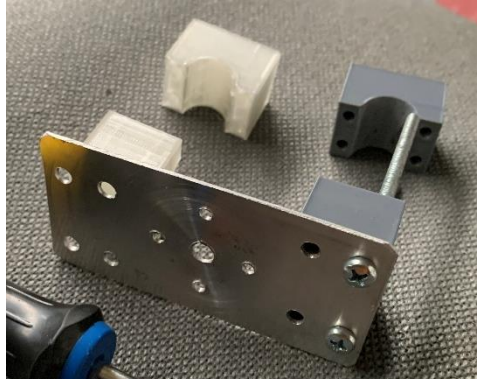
Sistema de anclaje de motor de cola [Fuente propia]
